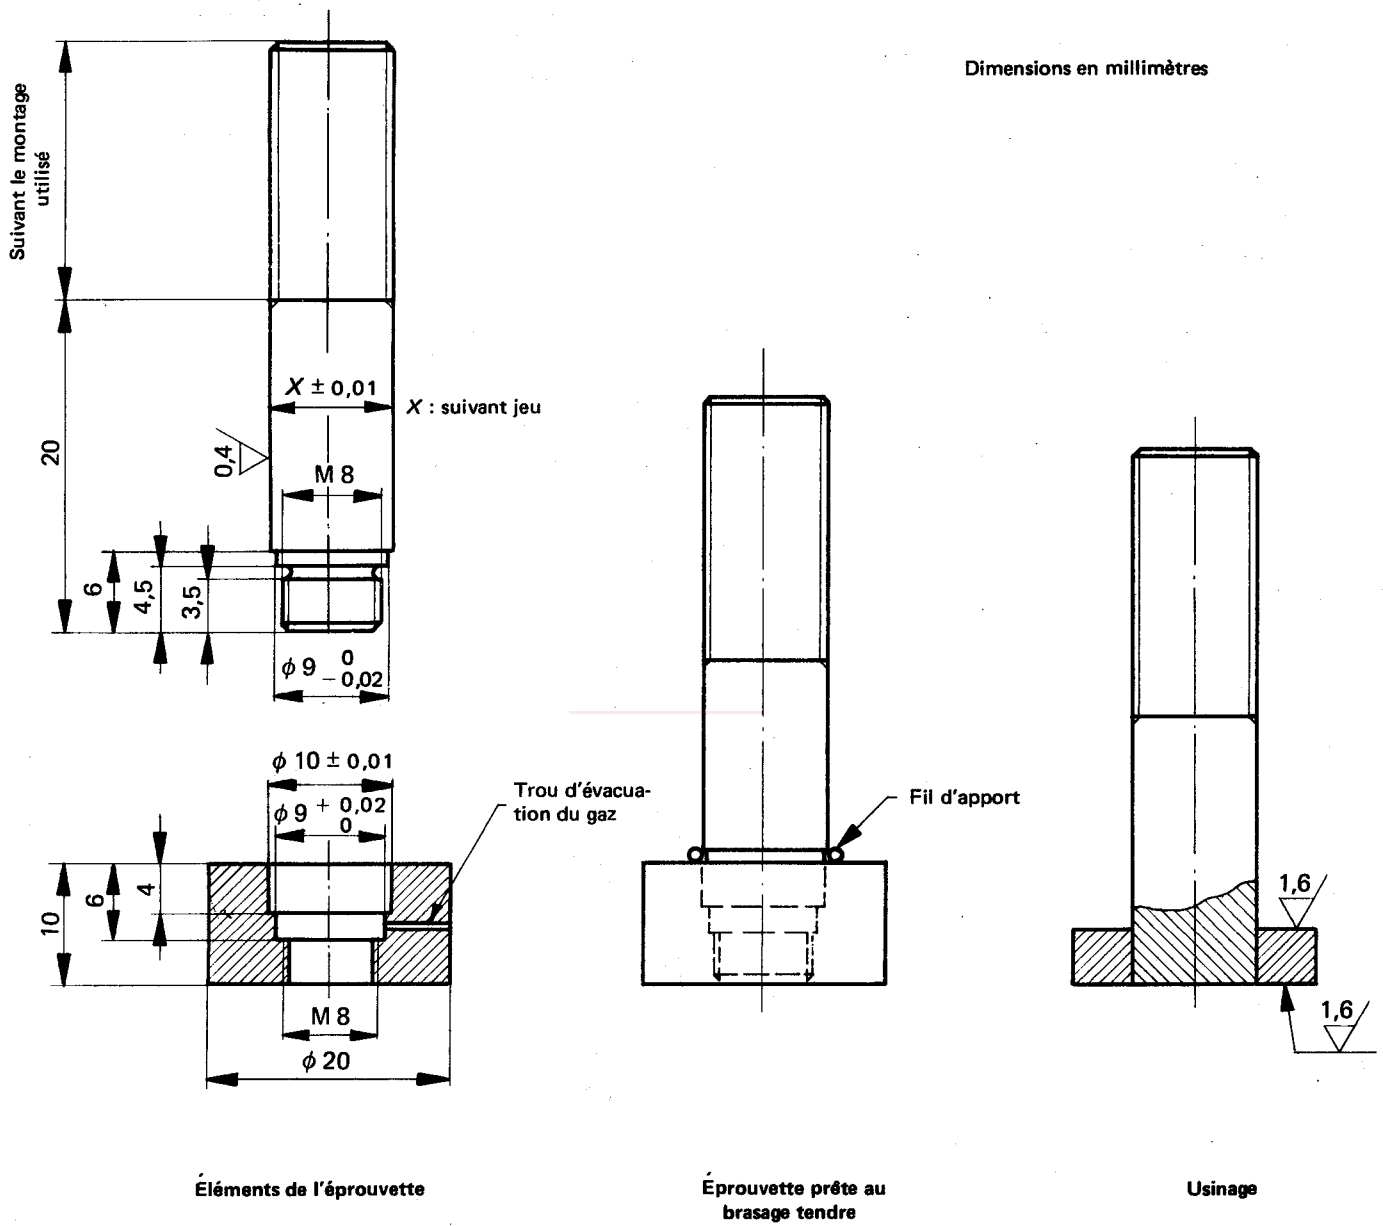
Dimensions de l'éprouvette de cisaillement type II
